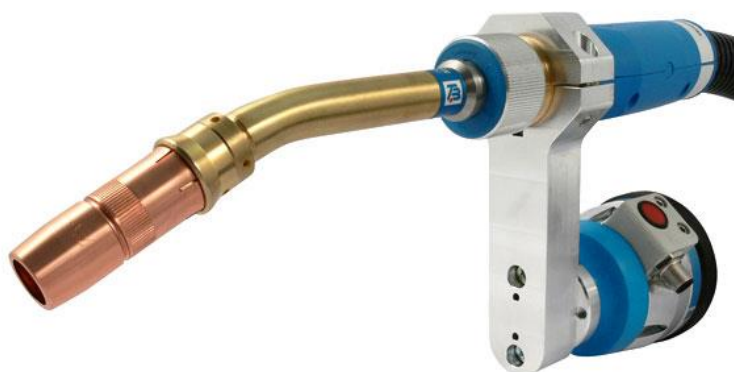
Сварочная горелка ТВi RM42G
